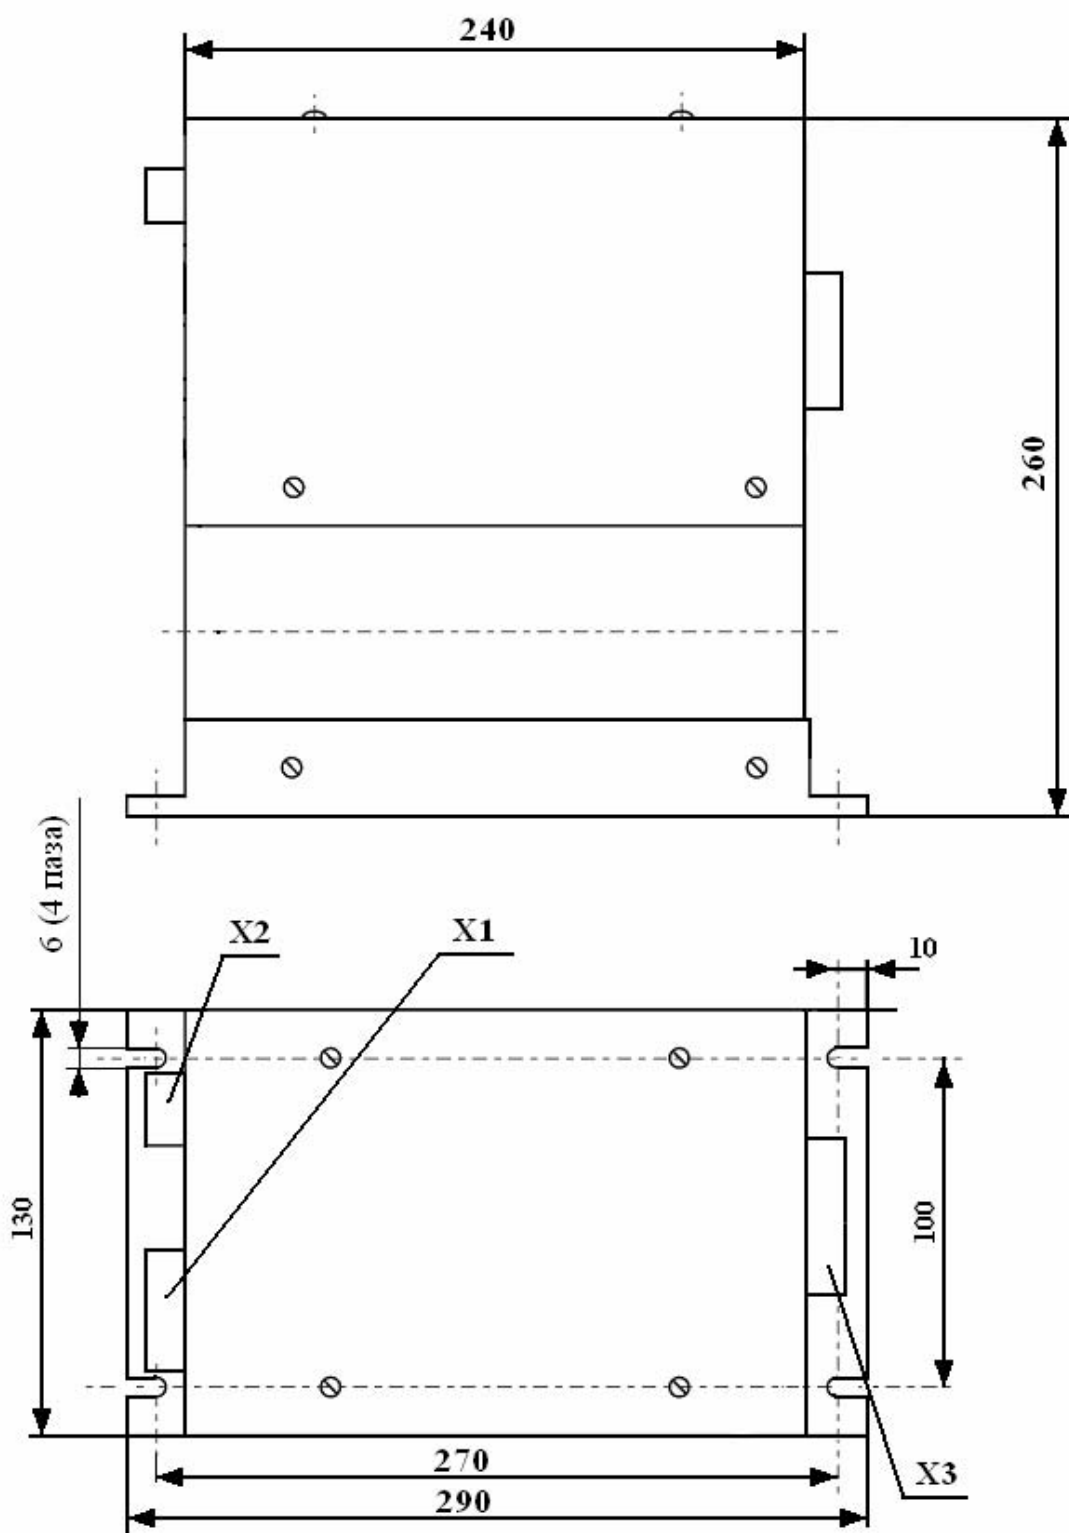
Габаритные размеры ПЕЛ-3-050-Е
